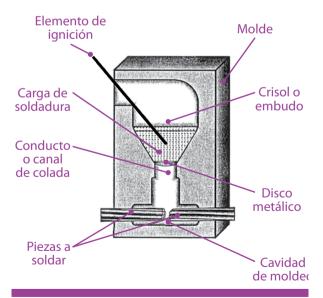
Vista en corte de un molde de soldadura con las piezas a soldarse
